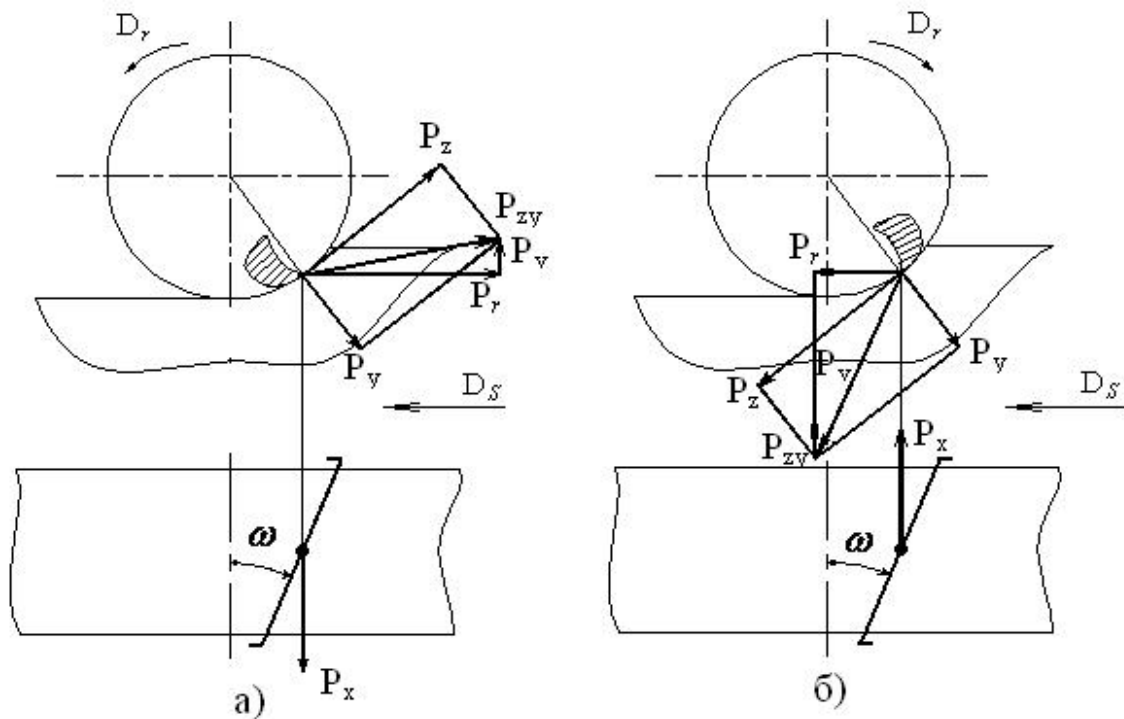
Силы, действующие на зуб цилиндрической фрезы:
